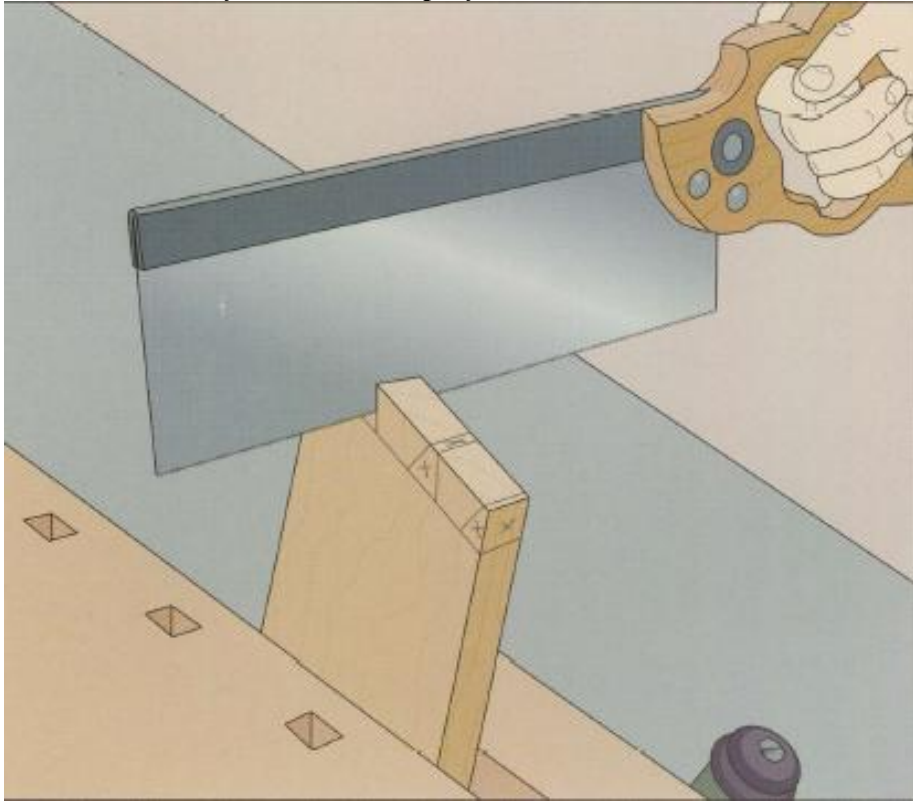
Kırlangıçkuyruğu diş boşaltması
